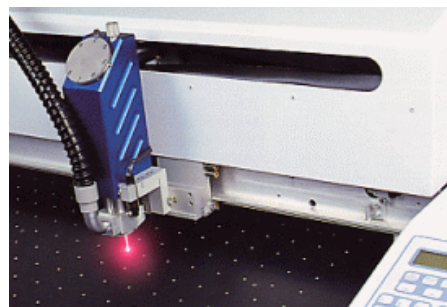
Testování a vyhodnocování prototypu (21)
